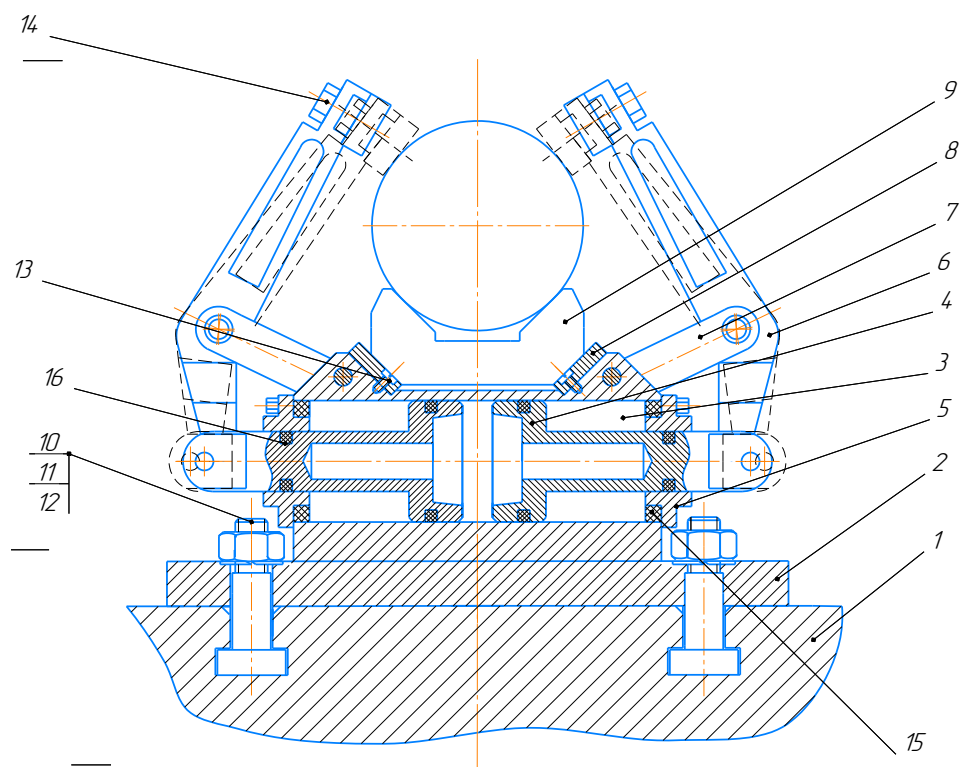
Станочное приспособление для фрезерной операции
